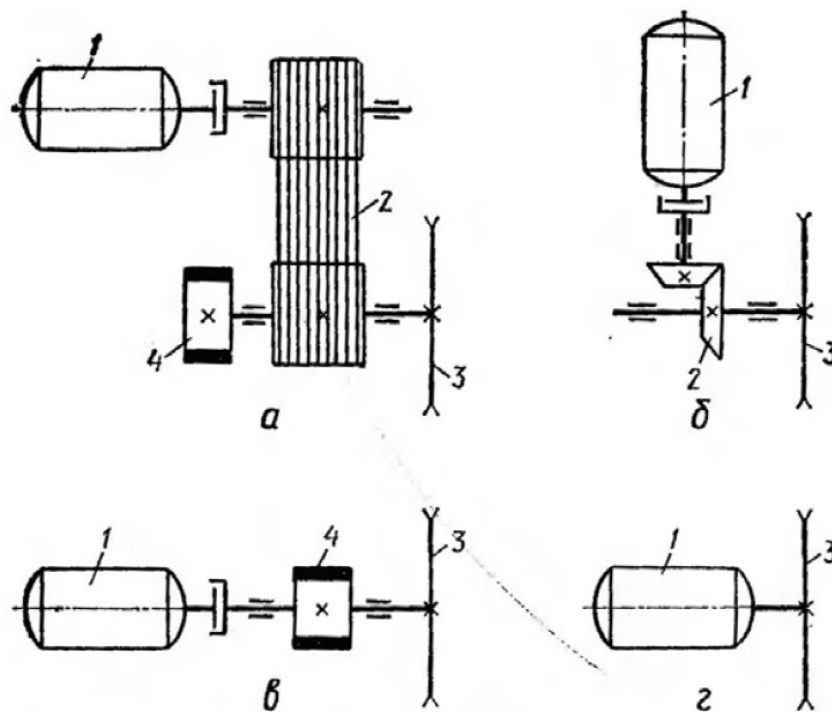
Схеми механізмів обертання диска пили: а – з клиноремінним приводом; б – з конічною зубчастою передачею; в – диск встановлений співвісно з електродвигуном; г – диск встановлений на валу електродвигуна
